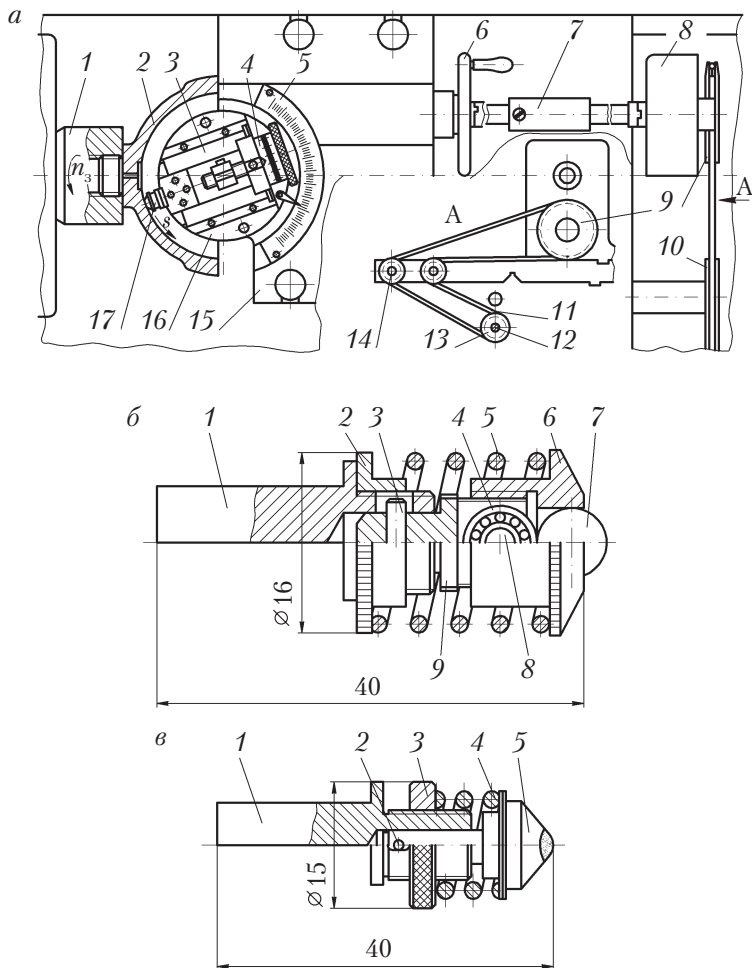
Схема комбинированной обработки чаш с помощью прецизионного устройства:
